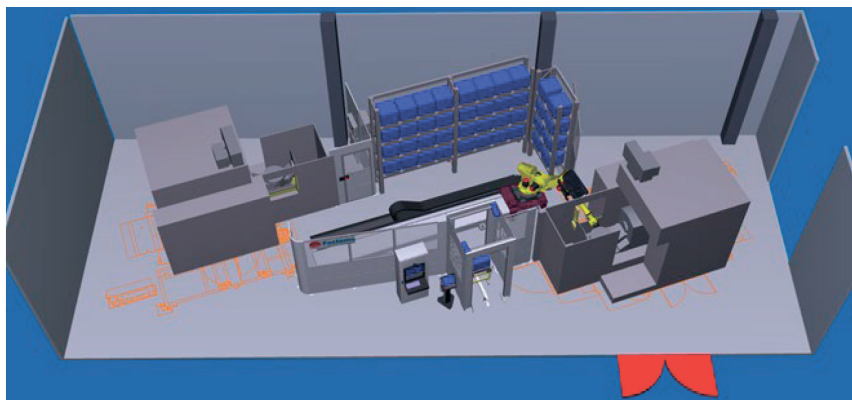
Автоматизированный участок с фрезерными обрабатывающими центрами
